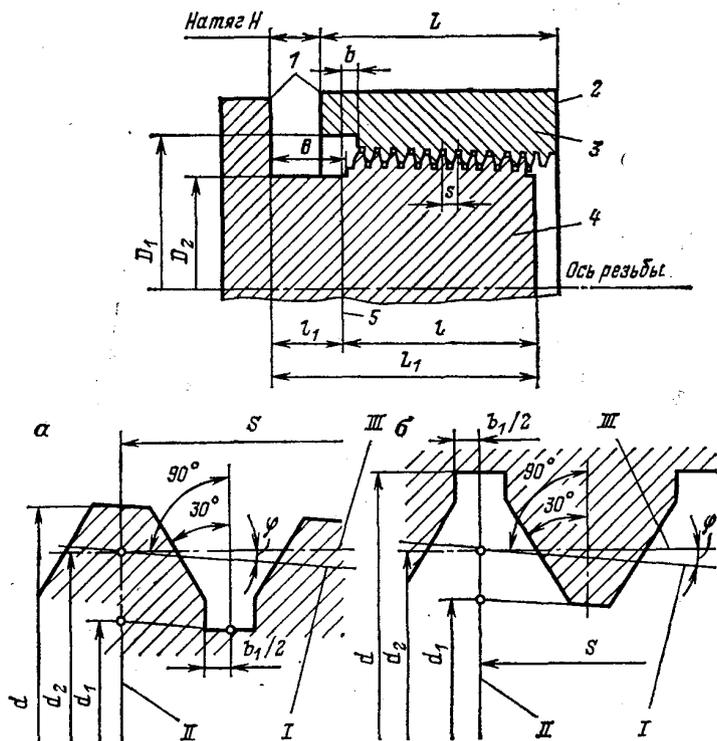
Резьбовые калибры для проверки трубной резьбы буровых труб и муфт к ним:
